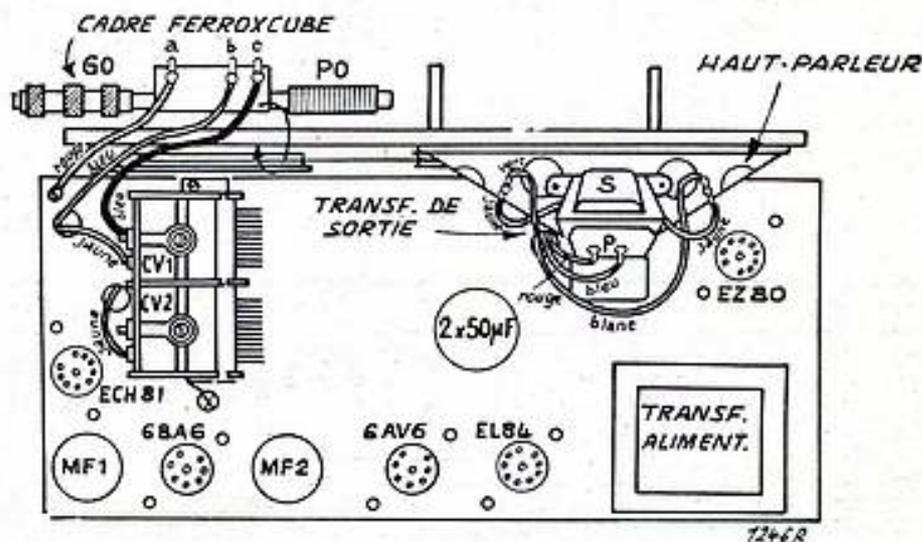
Dessus du châssis (disposition des pièces et câblage.)
